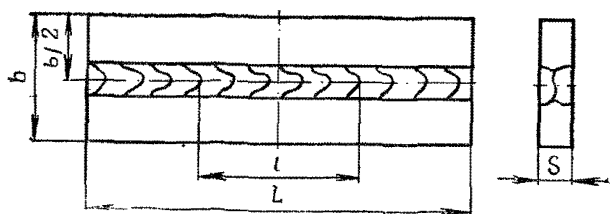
Форма и размеры плоского образца (разновидность), подготовленного для испытания сварного шва на загиб
